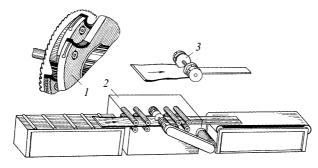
Фрезерно-обрезной станок: I – схема фрезы; 2 – схема станка; 3 – схема обработки необрезной доски фрезами
